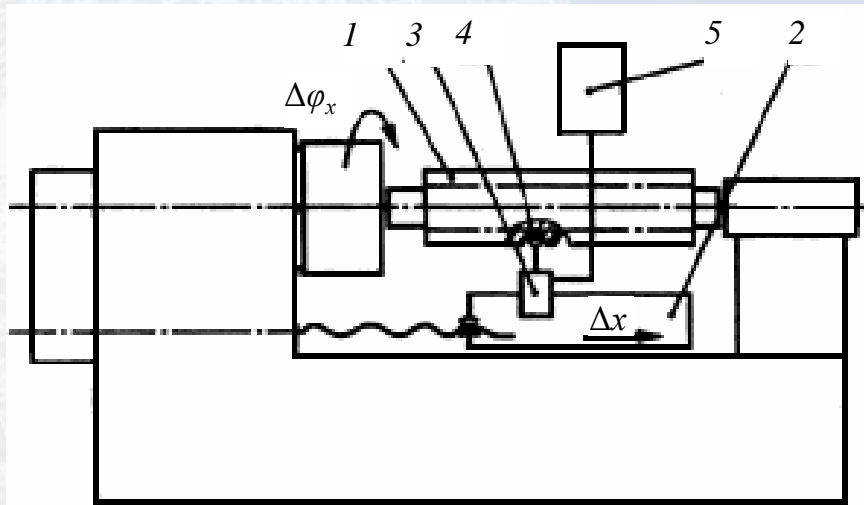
Схема измерения при помощи образцовой детали и датчика линейных перемещений:
